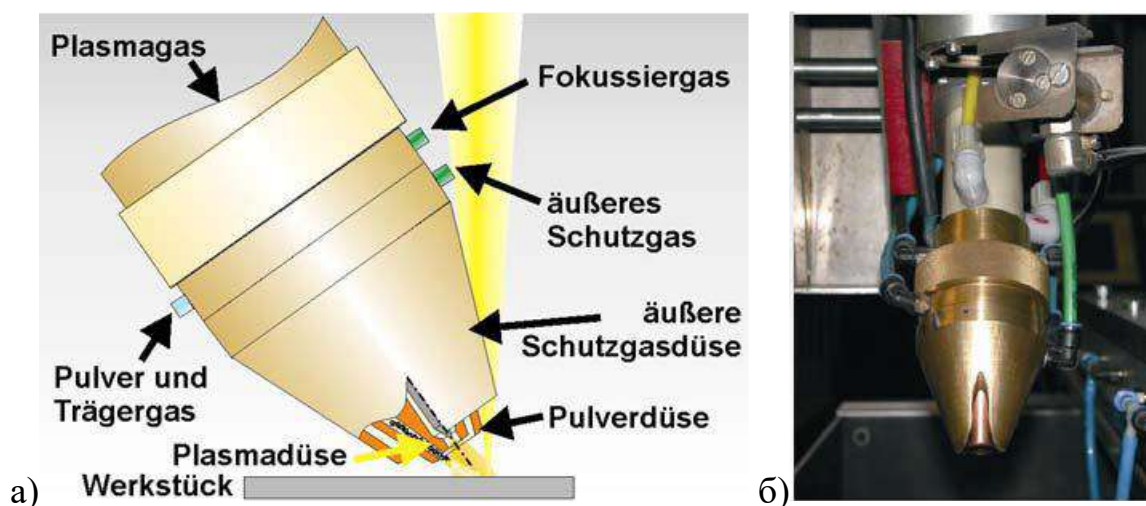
Схема (а) і зварювальна головка (б) для лазерно-плазмового зварювання із використанням присаджувальних порошкових матеріалів [83].
